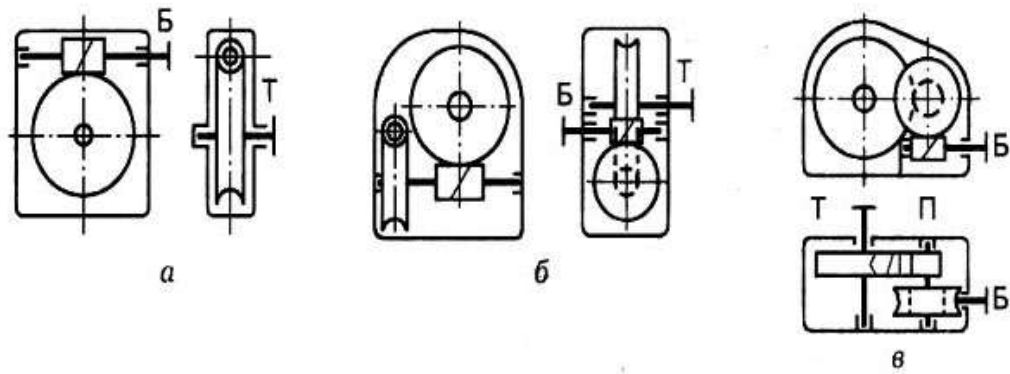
Схемы червячных редукторов: а — одноступенчатый; б — двухступенчатый; в — червячно-цилиндрический
